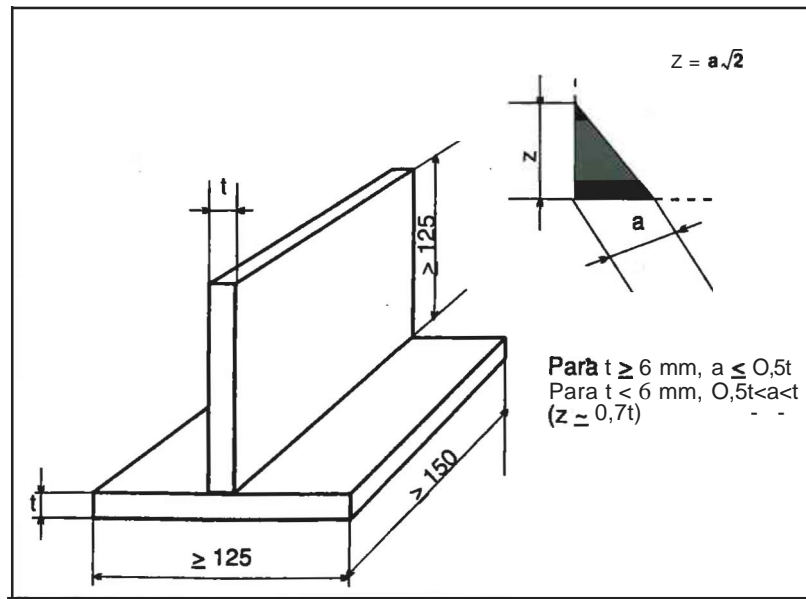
DIMENSIONES DEL CUPÓN DE PRUEBA PARA EL SOLDEO DE CHAPAS EN ÁNGULO (DIMENSIONES EN MILÍMETROS)
